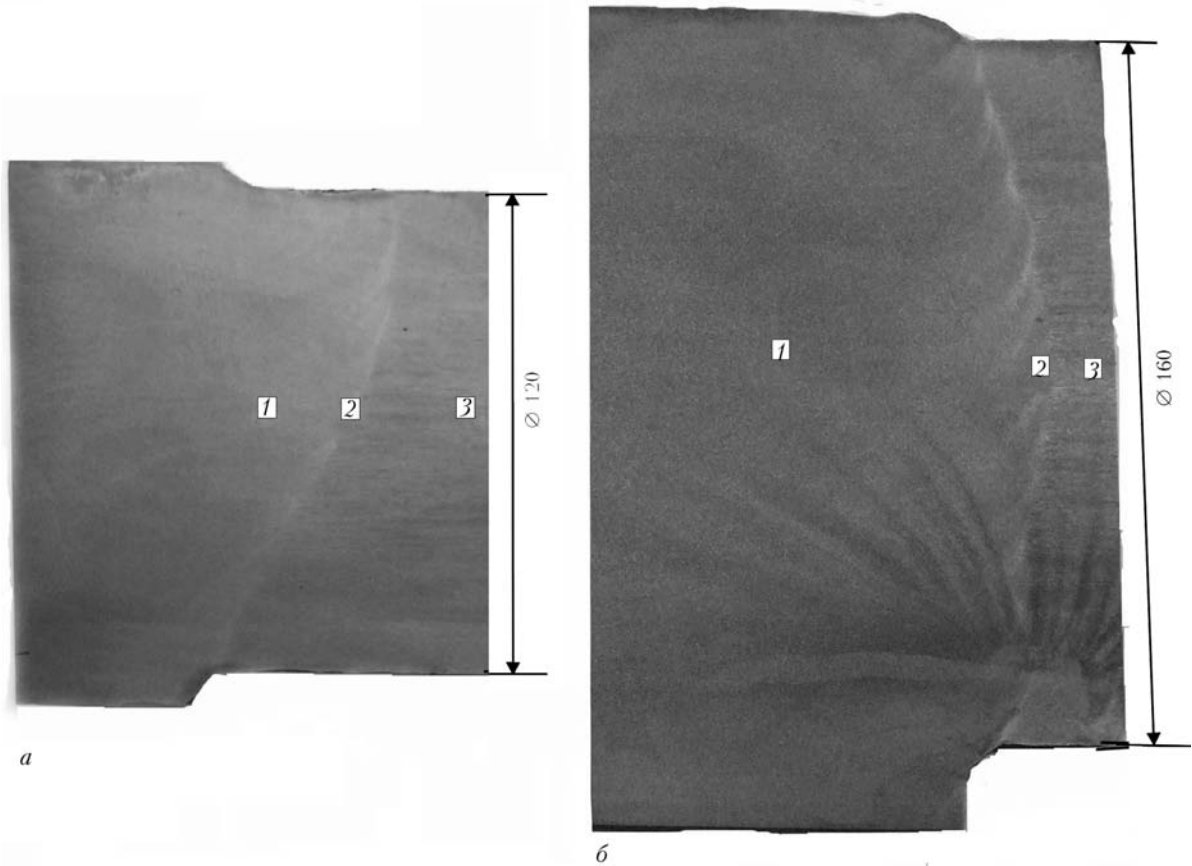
Макрошлифы зоны соединения патрубка с литым корпусом задвижки Ду50 (а) и Ду80 (б): 1 – литой электрошлаковый металл; 2 – линия сплавления; 3 – зона термического влияния на металле патрубка
